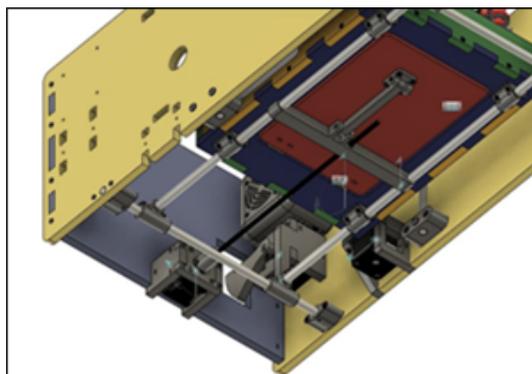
Печатный станок для слабовидящих (вид сверху)
